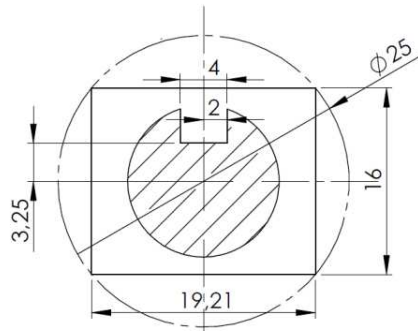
Dimensiones del chavetero (cotas en milímetros).
